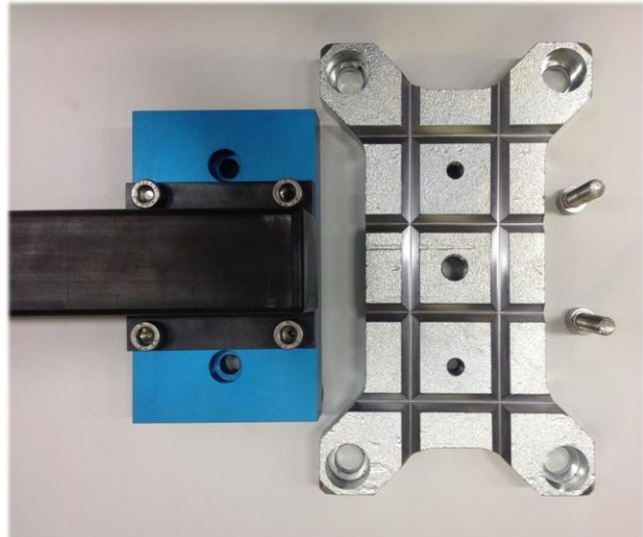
Modifierad BoxJoint-platta och adapterplatta (ovanifrån)
